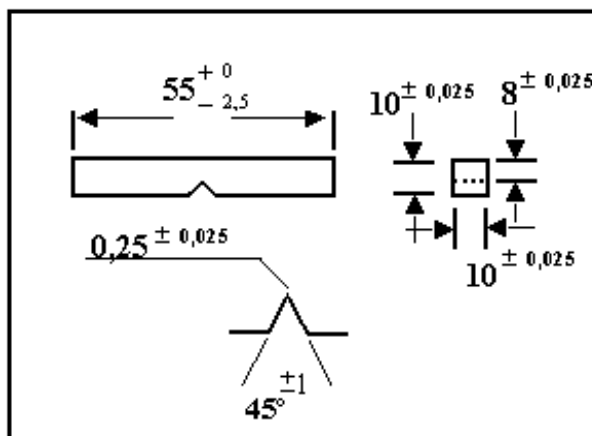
Corpos-de-prova para ensaios de impacto tipo Charpy (dimensões em mm).
